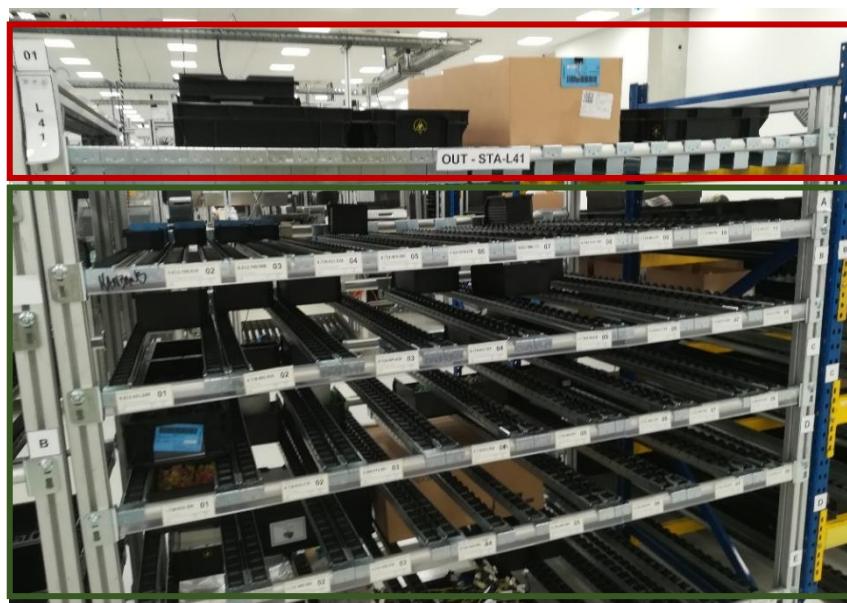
Ponto de vista do supermercado pelo Milk Run, rampa in (verde) e out (vermelho)
